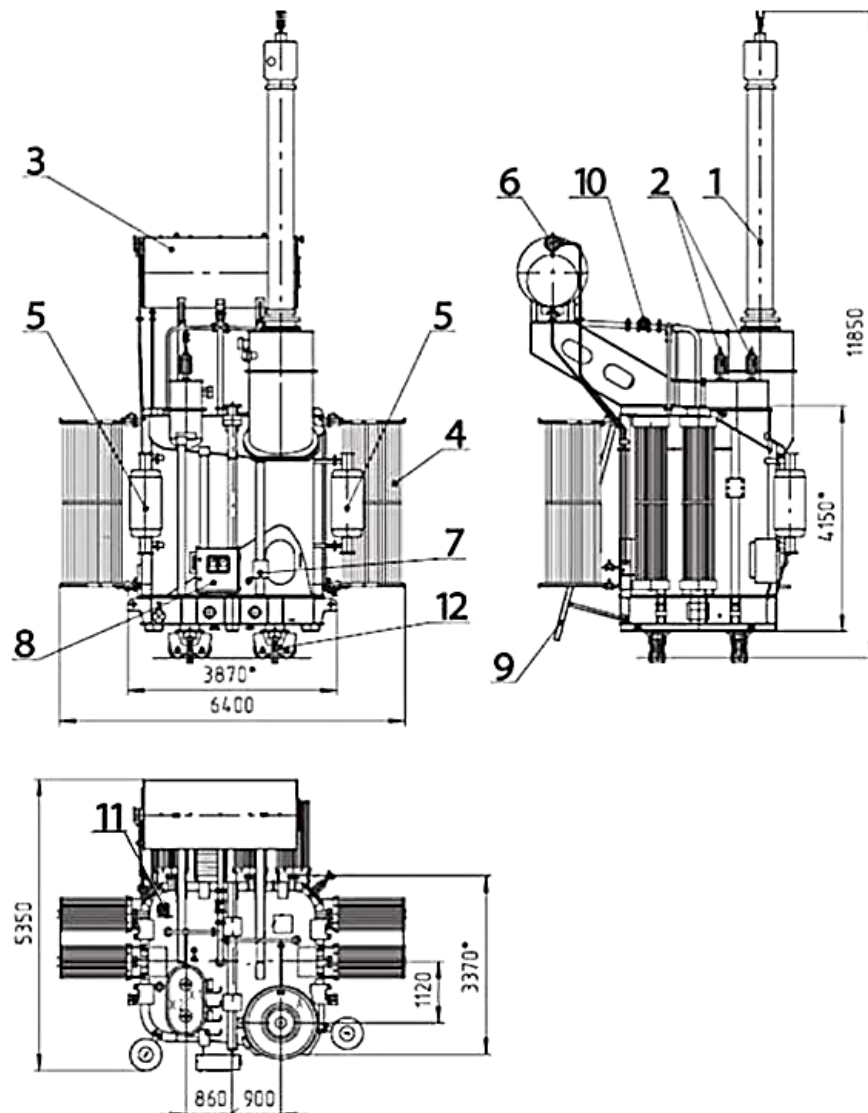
Загальний вигляд та габаритні розміри реактора типу
